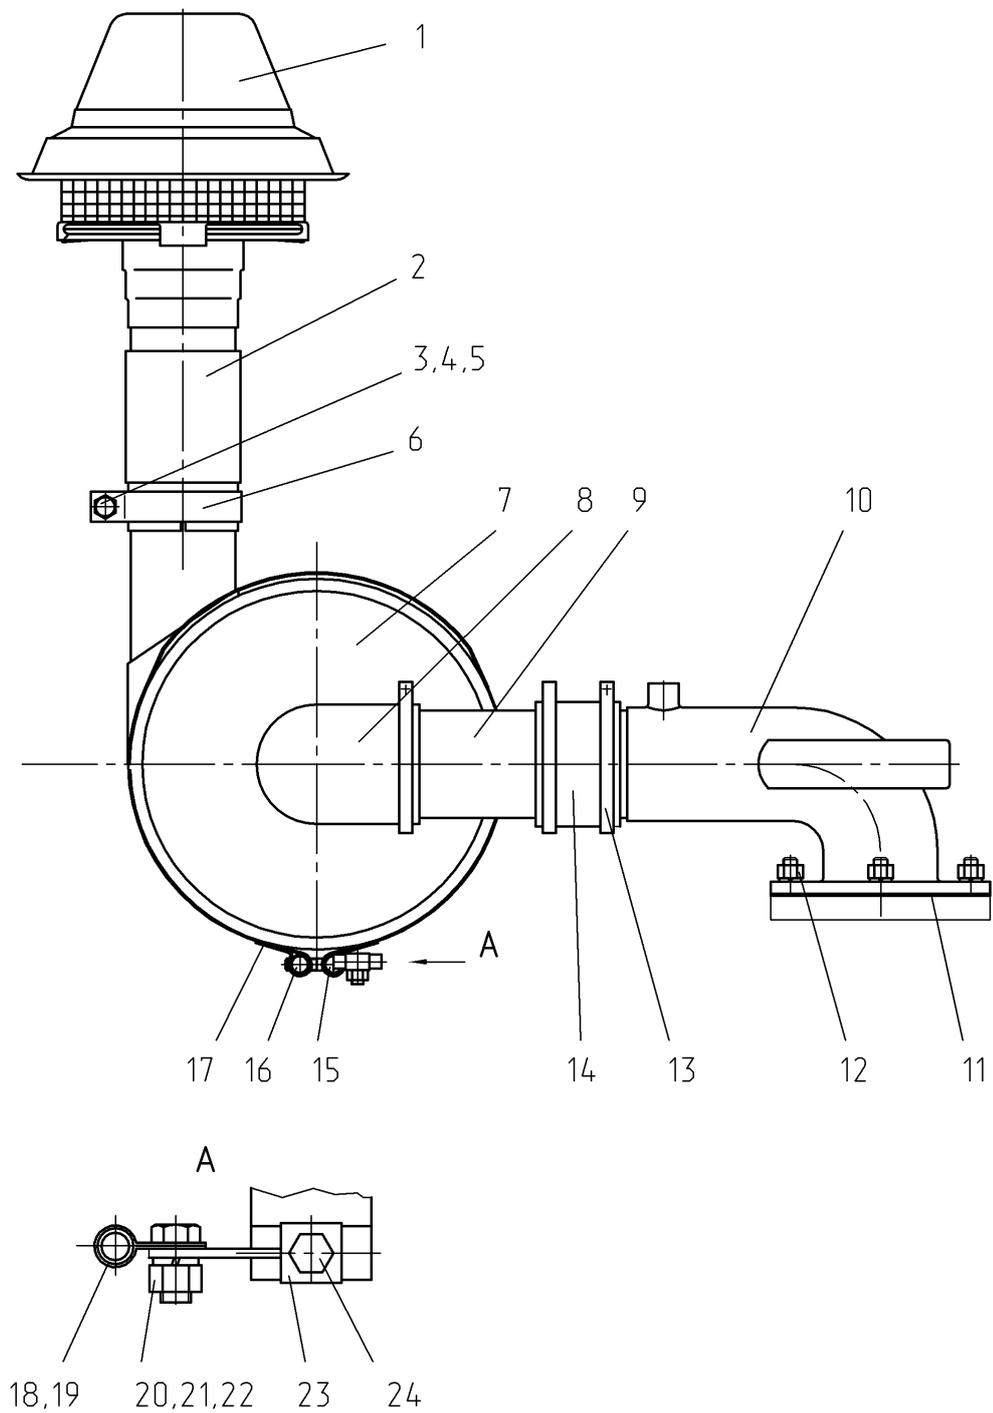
Установка воздухоочистителя 237.02.04.00.000
